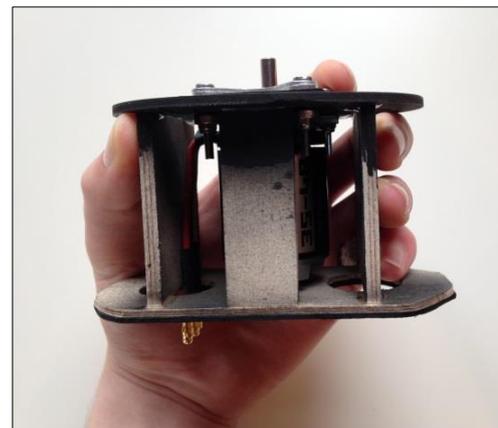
fertige Motoraufhängung bereit für den Einbau ins Flugzeug
